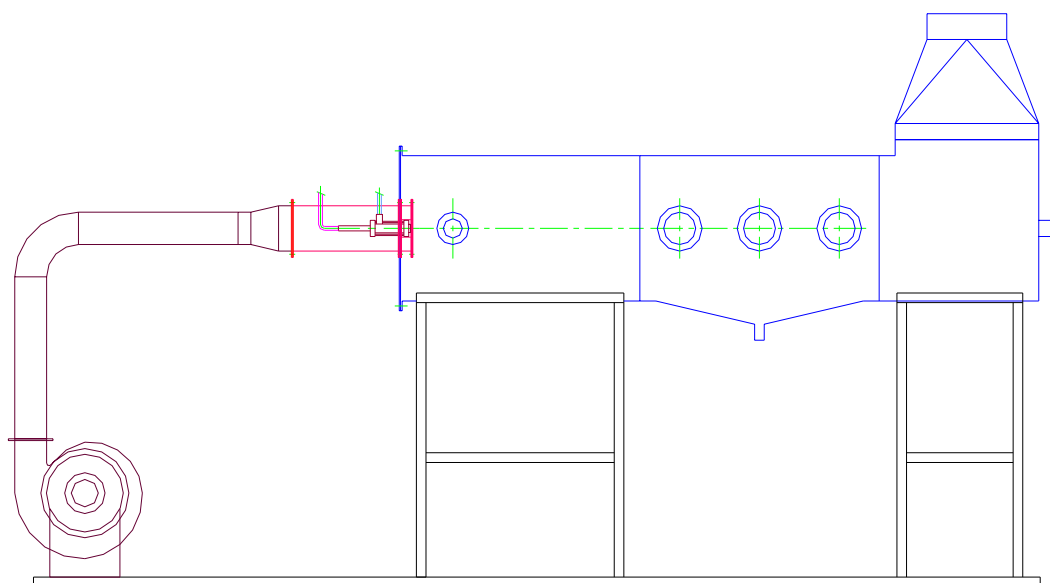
Fornalha provisória para realização de ensaios preliminares de queima.
